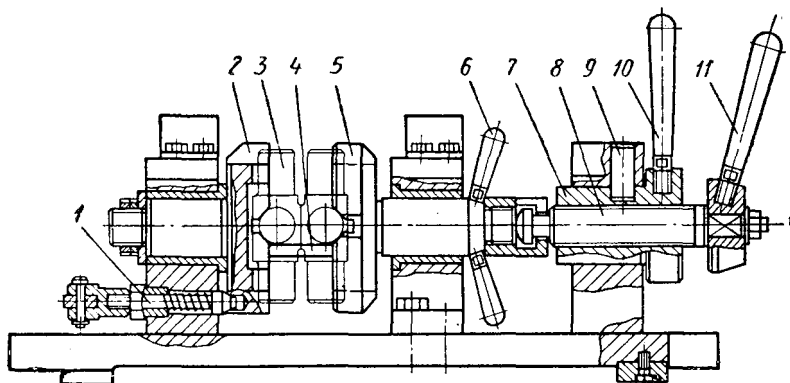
Приспособление поворотное для прорези смазочной канавки на концах крестовин
